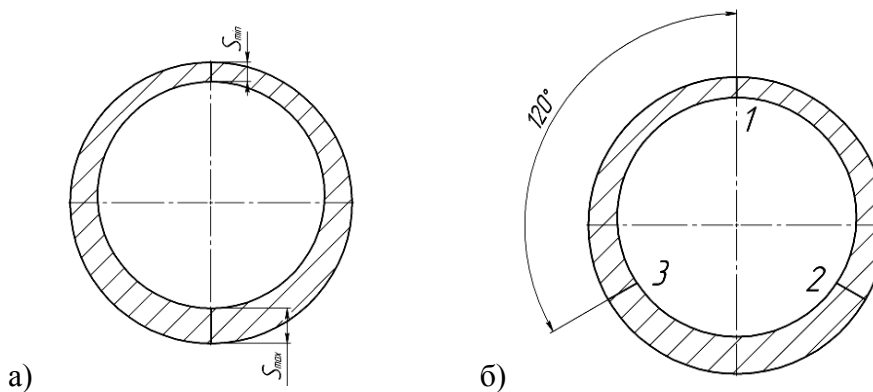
Вид поперечных сечений исследуемых заготовок: а) принципиальный вид исходной заготовки трубного сортамента; б) схема расположения продольных расчетных сечений для заготовок DN32
